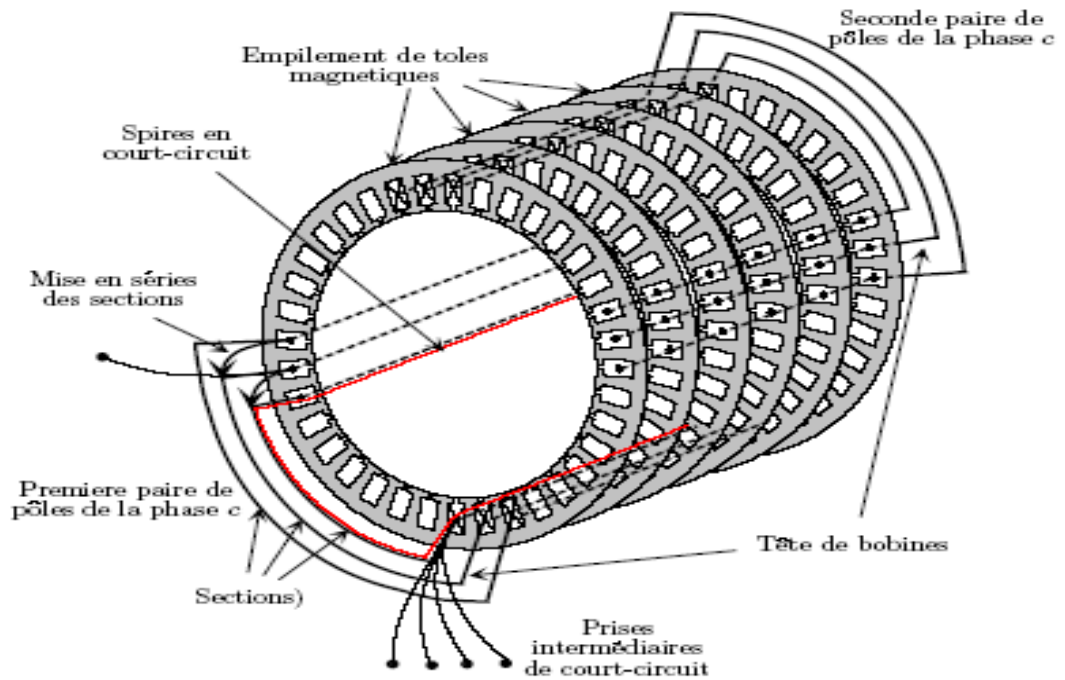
Vue schématique du stator (circuit magnétique, conducteurs d'encoches, tête de bobines, Enroulement statorique d'une machine a 4 pôles). [1]
